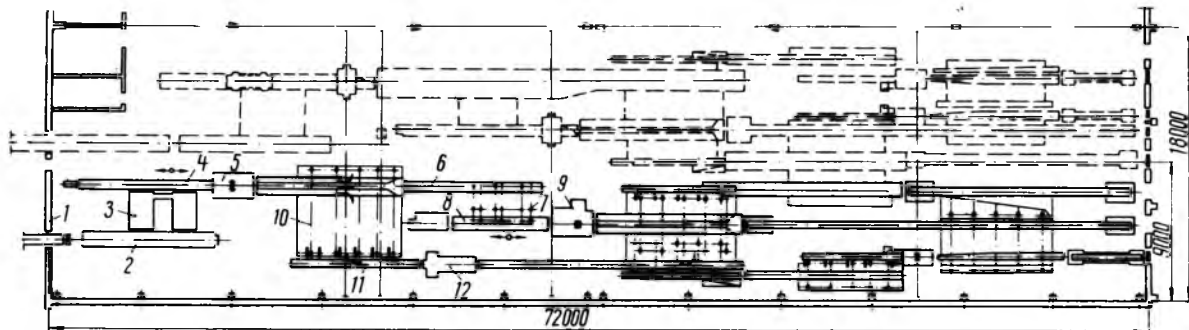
Линия круглопильных станков на базе двухпильного станка с симметрично раздвигающимися пилами
